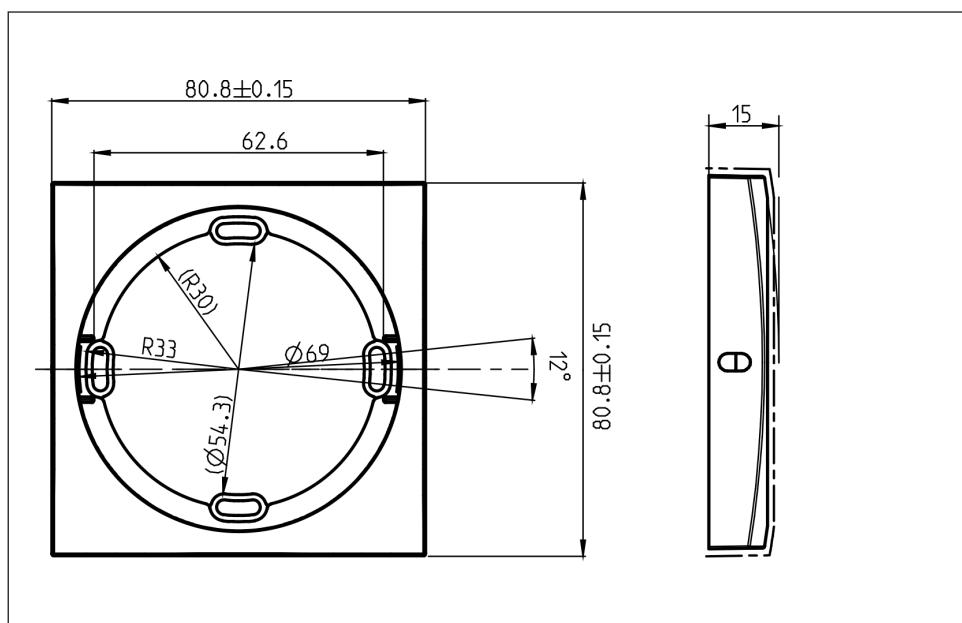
Fiche technique du cadre du lecteur WRU 200 (vue de dessus et vue de côté)
